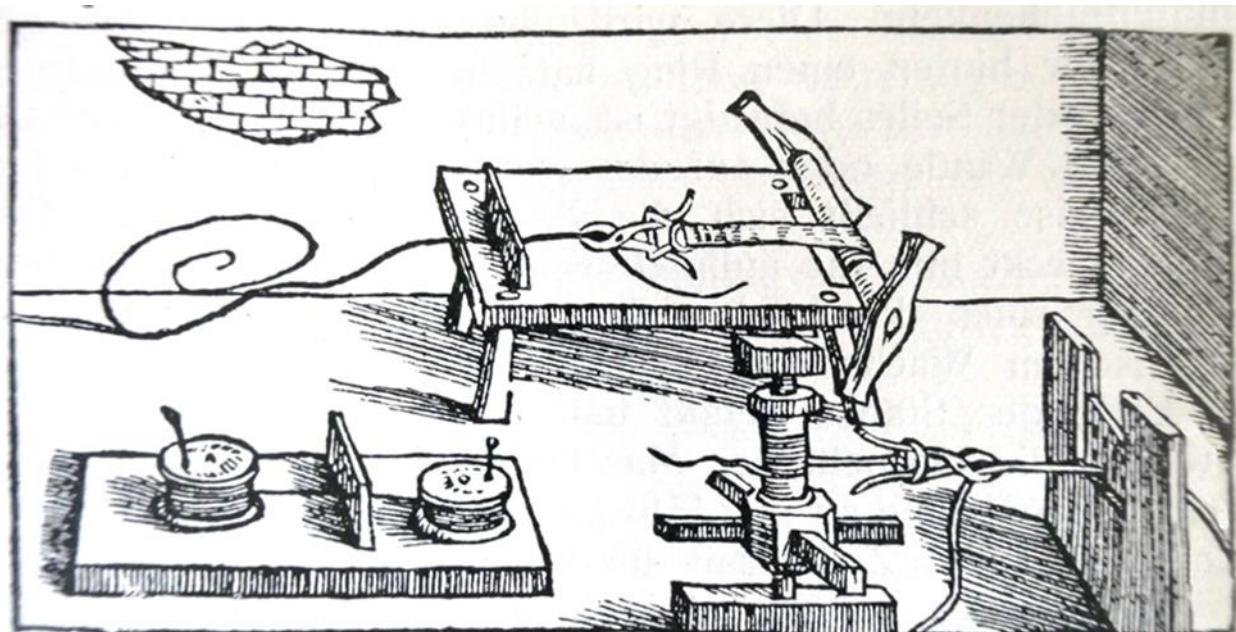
Drahtziehen mit Haspeln und Rolle.
